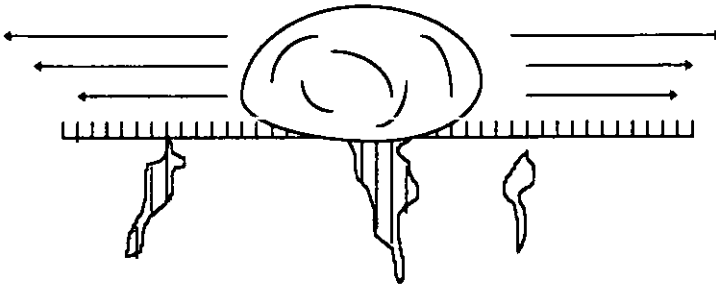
Remoción del exceso de penetrante, con un movimiento de vaivén; cuidando de no extraer el penetrante de posibles discontinuidades.
